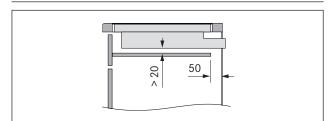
Vista laterale piano di protezione cavi e aerazione
